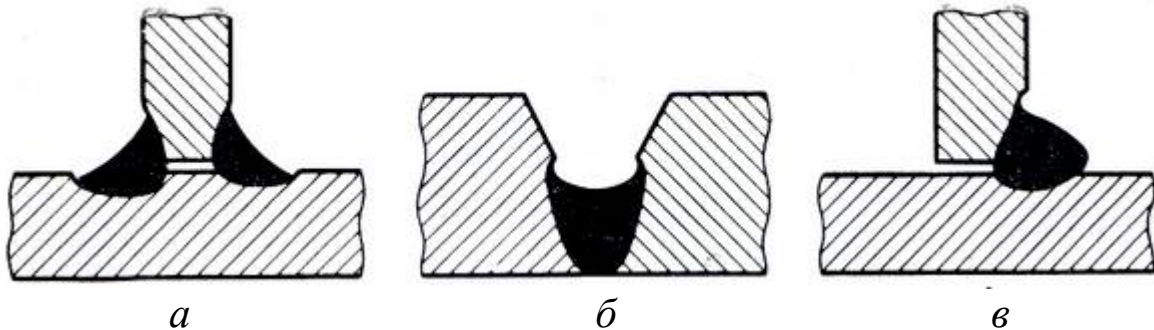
Подрезы: *а* – двусторонний при сварке углового шва; *б* – двусторонний при сварке первого слоя многослойного стыкового шва; *в* – односторонний с наплывом на вторую кромку при сварке углового шва
